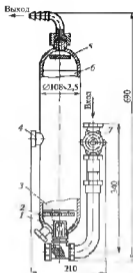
Конструкция предохранительного жидкостного затвора ЗСП-3 для азотлана среднего давления: 1 — обратный клапан; 2 — распределительный колпачок; 3 — рассекатель; 4 — пробка; 5 — отбойник; 6 — корпус; 7 — вентиль
